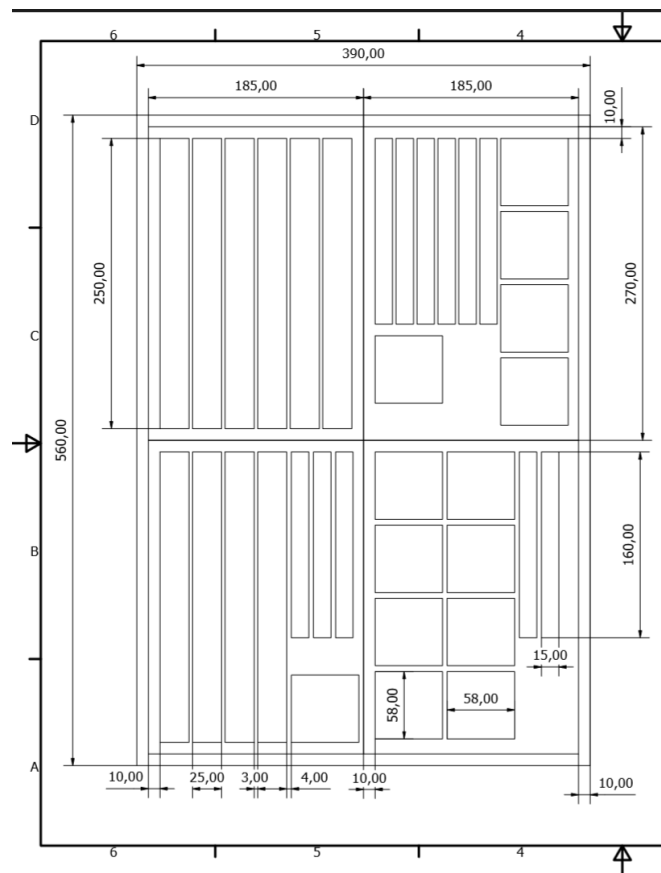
Plano completo de tablero de las probetas de tracción, flexión e impacto
